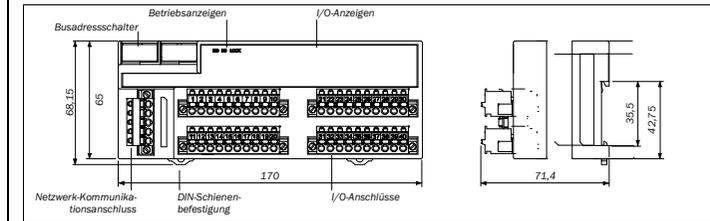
Maßbild UE4421-22EE900 und UE4421-22EE490 (mm)
